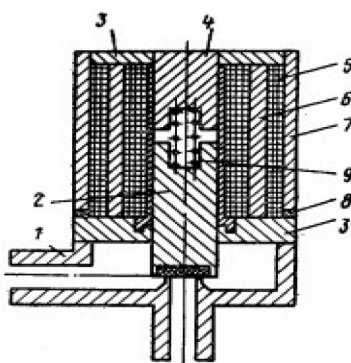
Клапан: 1-корпус с седлом, 2-якорь запорного органа, 3-два фланца, 4-стопа, 5-электромагнит, 6-постоянный магнит, 7-кожух, 8-немагнитная вставка, 9-пружина
